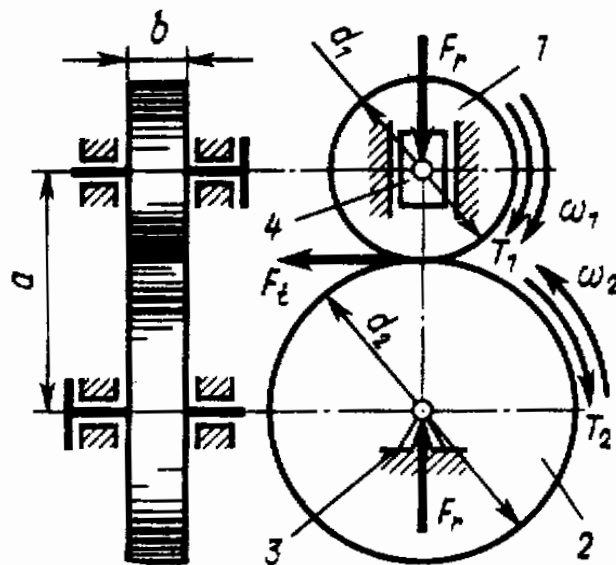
Схема фрикционного механизма: 1- ведущий каток; 2 – ведомый каток; 3 – неподвижная опора; 4 – подвижная опора
